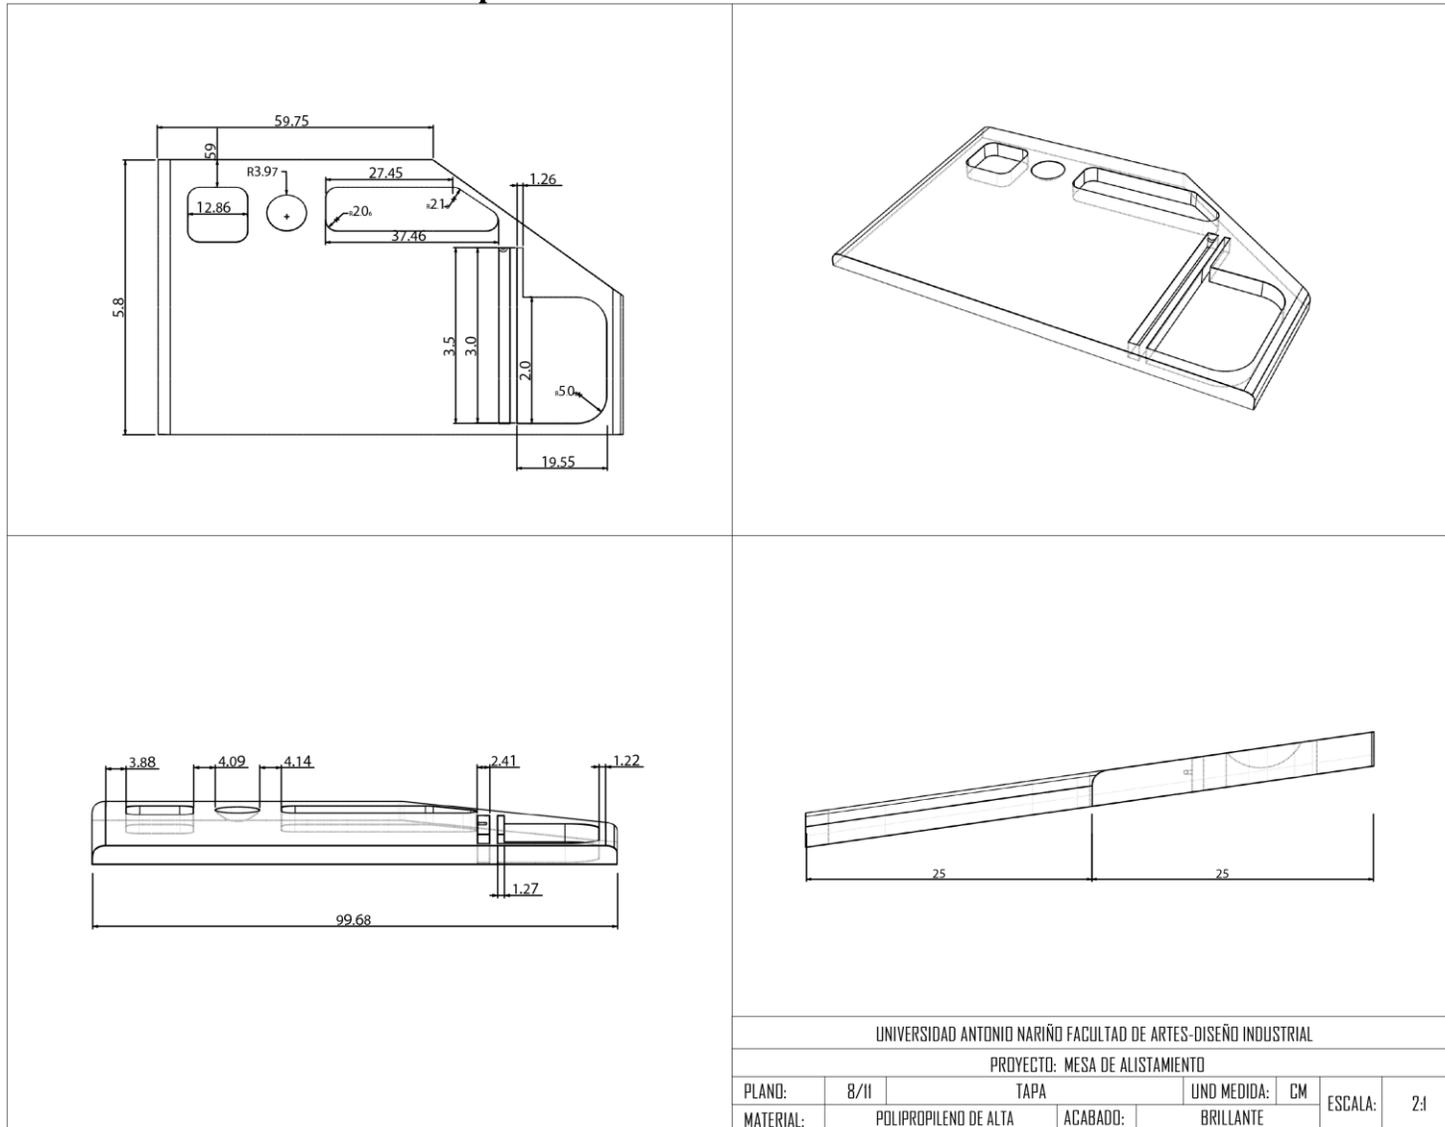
Planos de piezas 1 (Elaboración propia, 2020)
